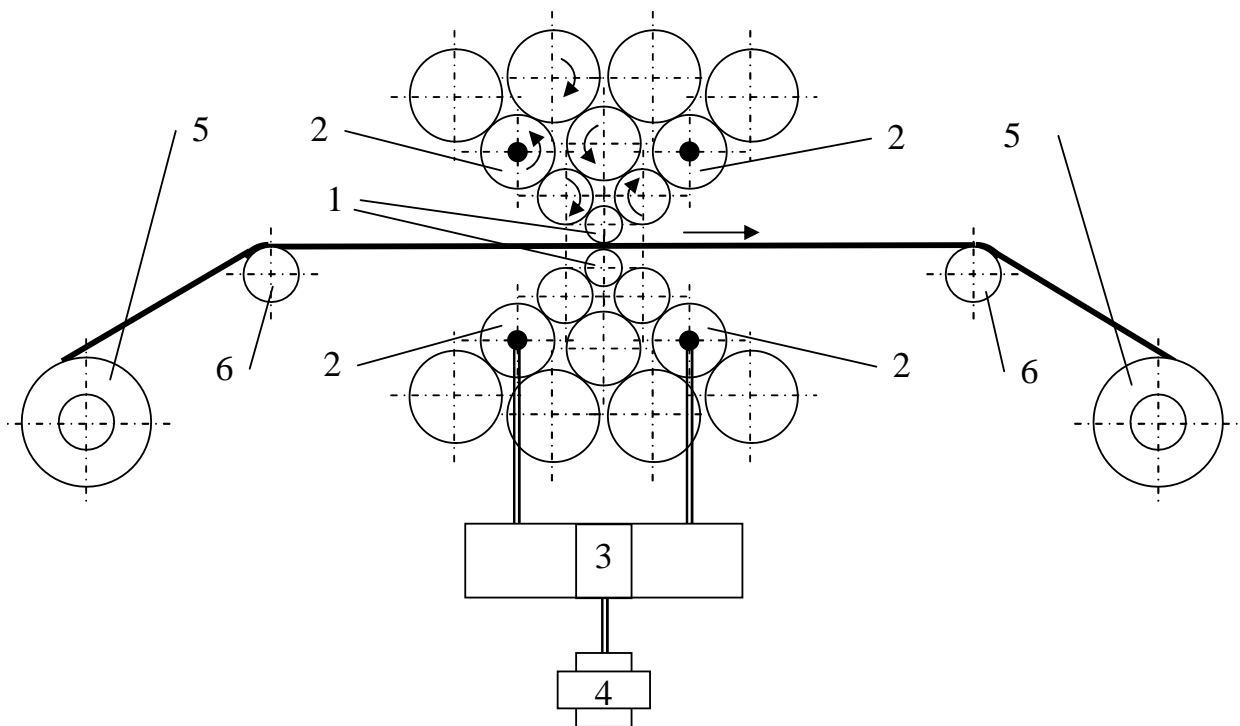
Схема багатовалкового реверсивного стану холодної прокатки:
